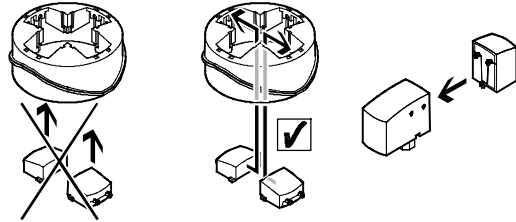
Emboîtement des pièces de l'anneau indicateur
